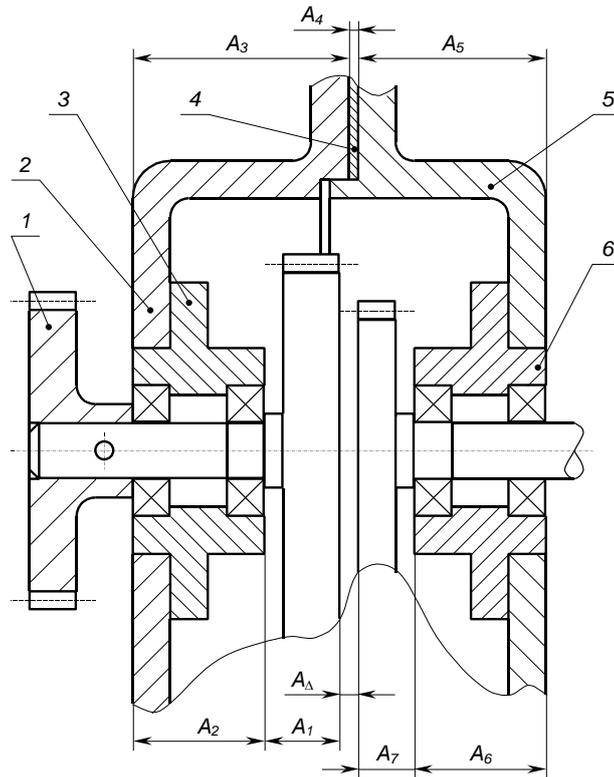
Часть сборочного чертежа механизма:
